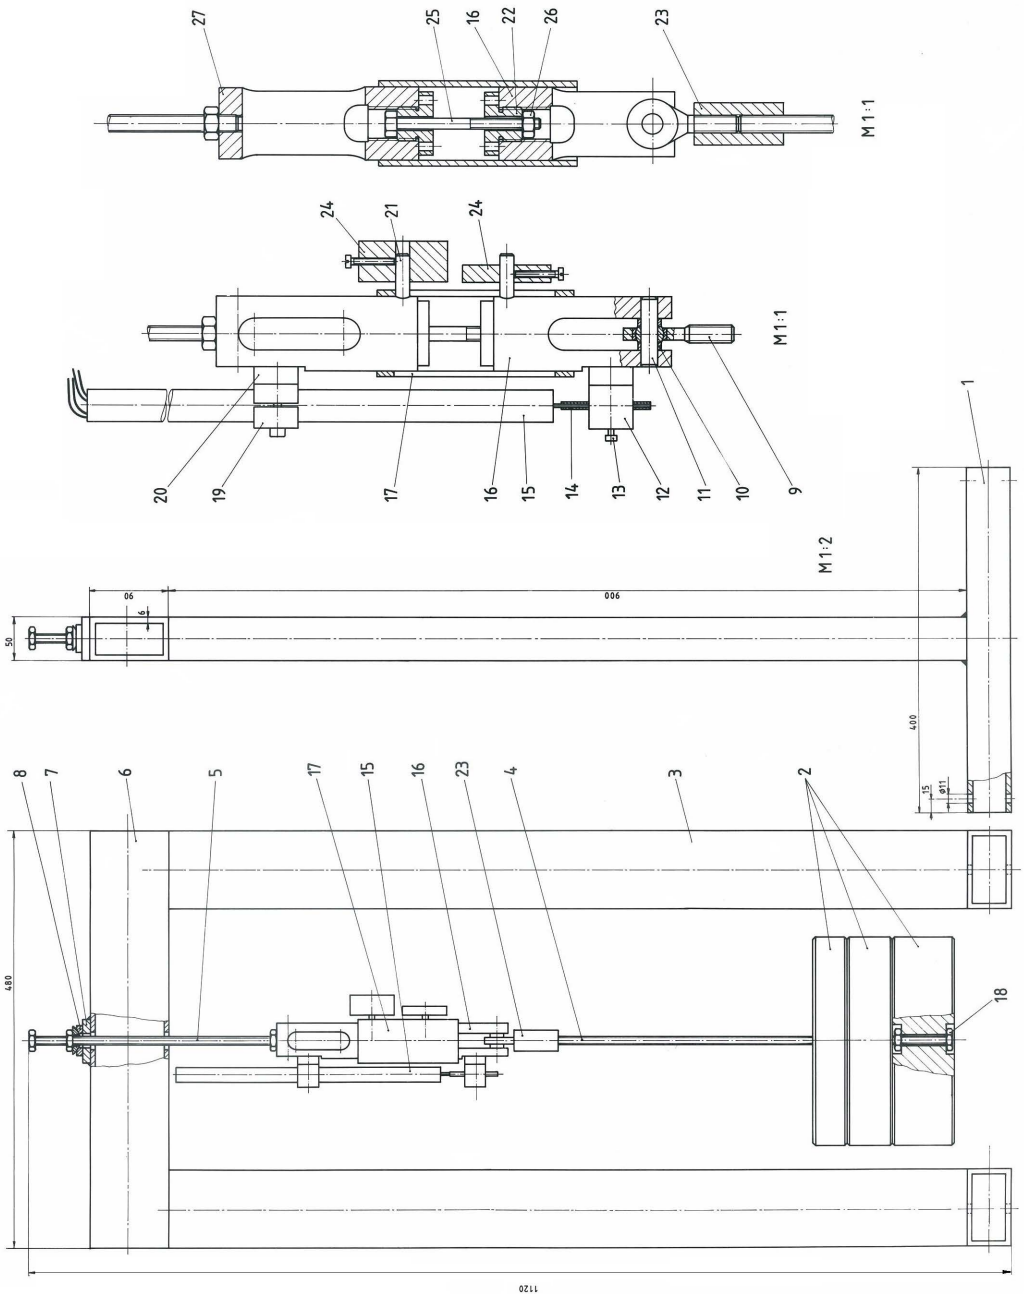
Prüfvorrichtung für Schrauben mit Muttern zur
